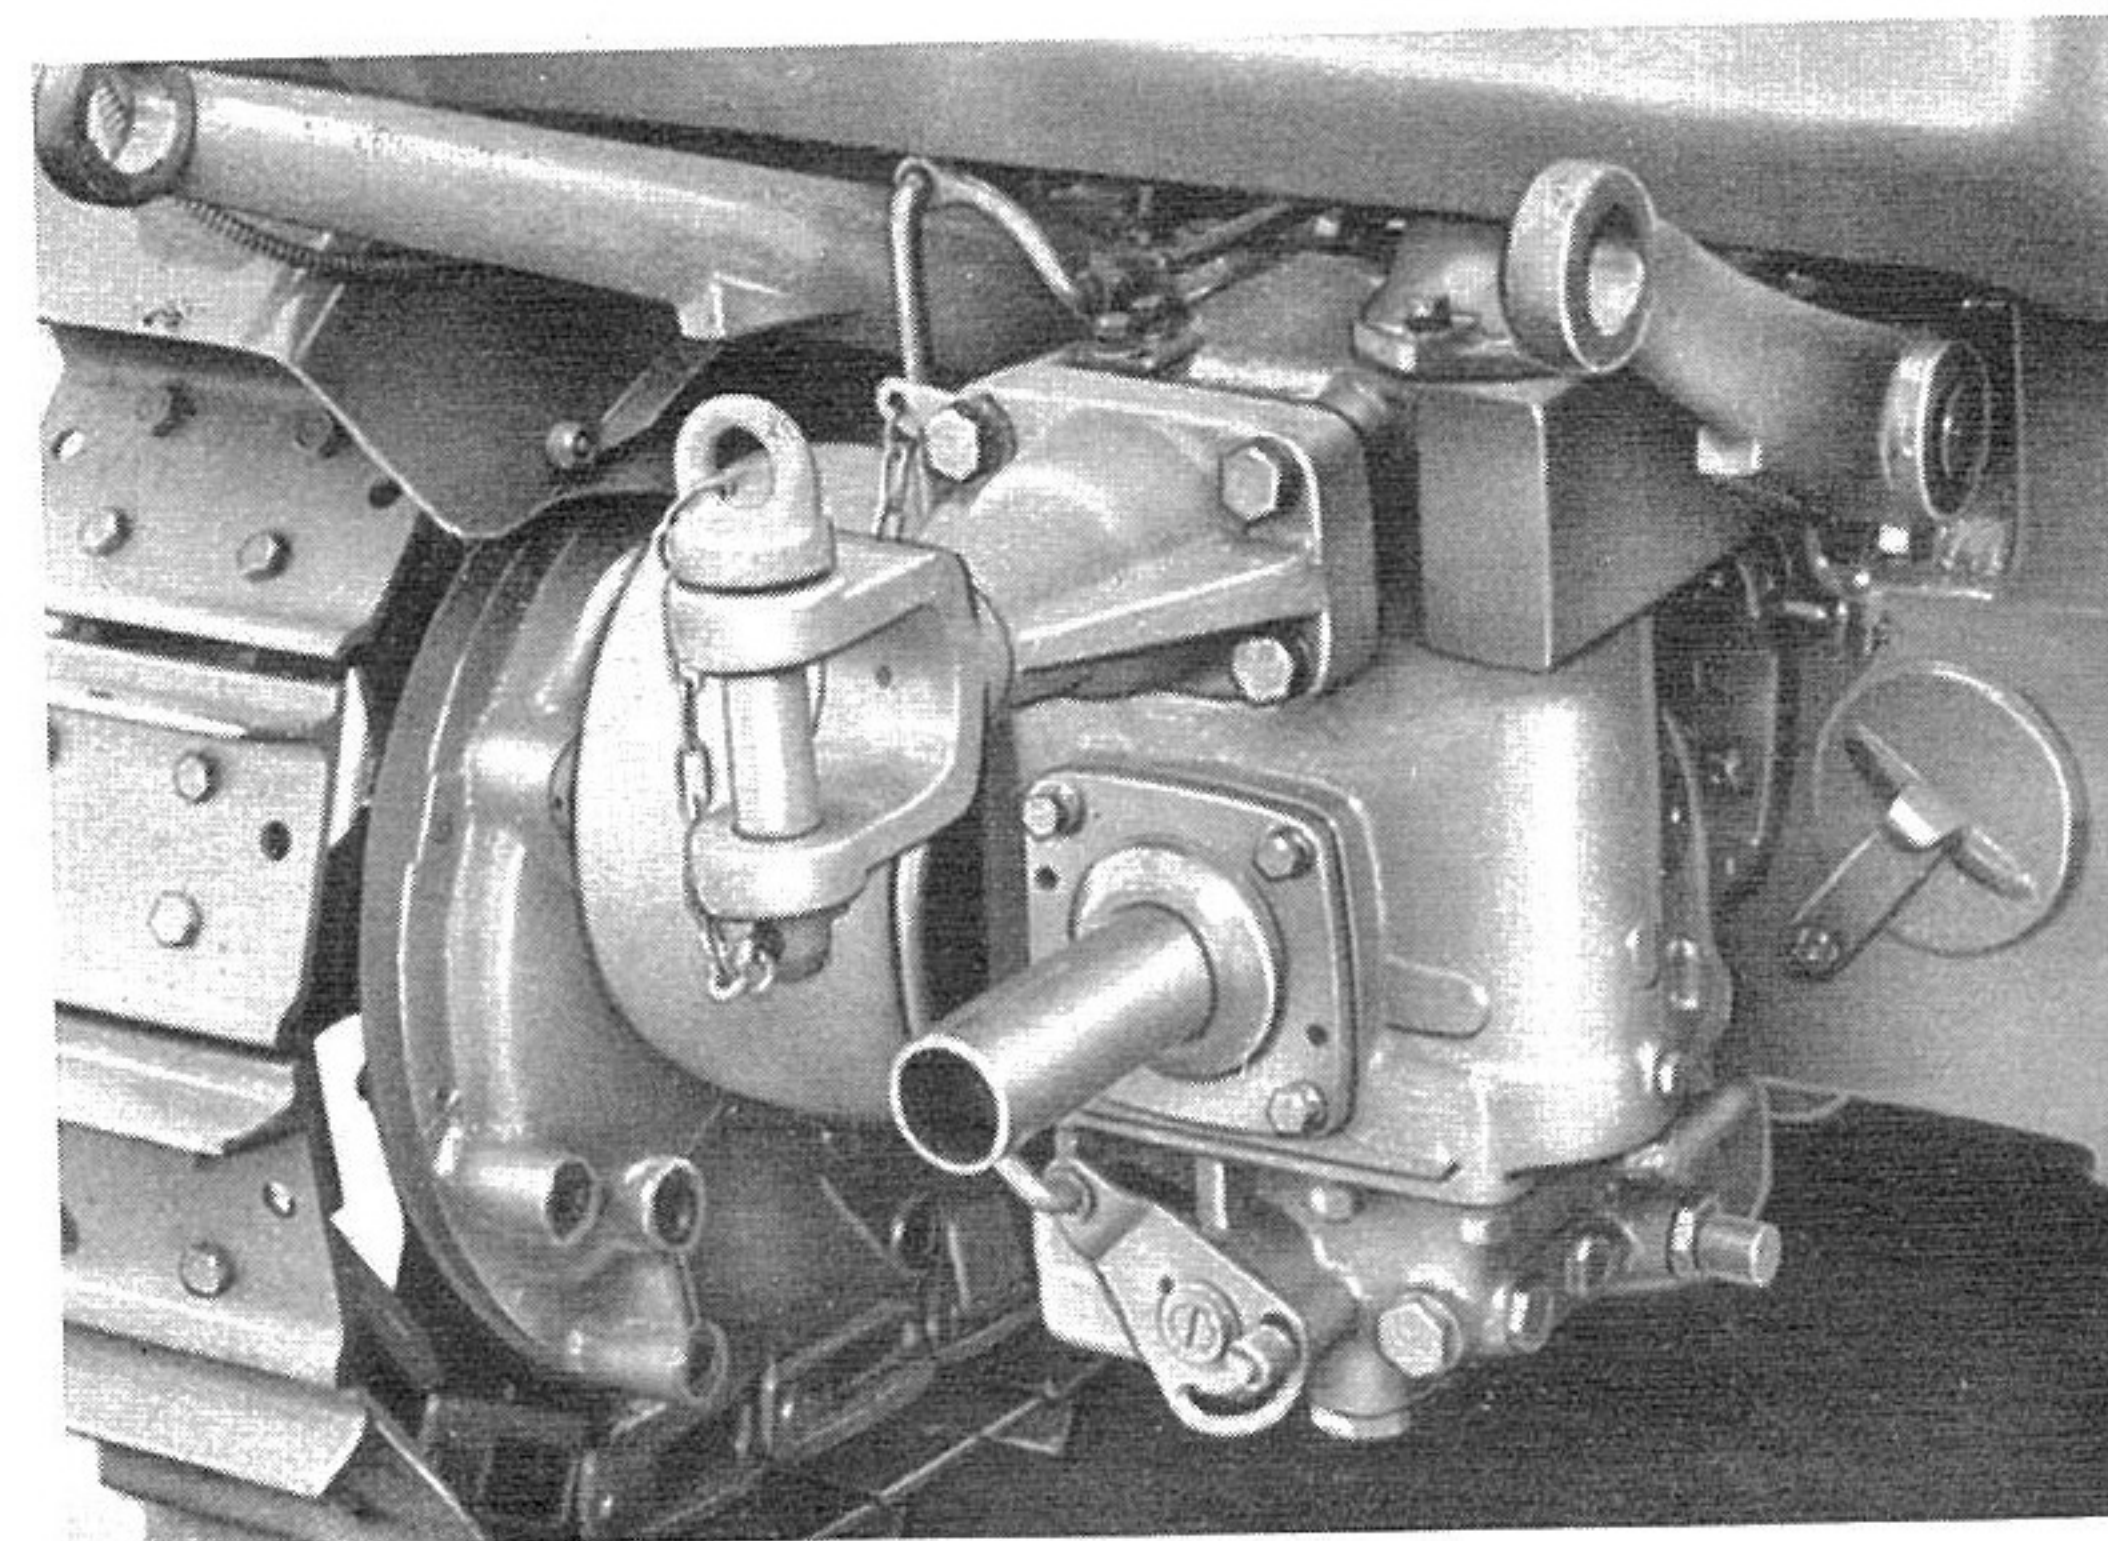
Crochet de remorquage monté sur le carter du dispositif de relevage hydraulique.
